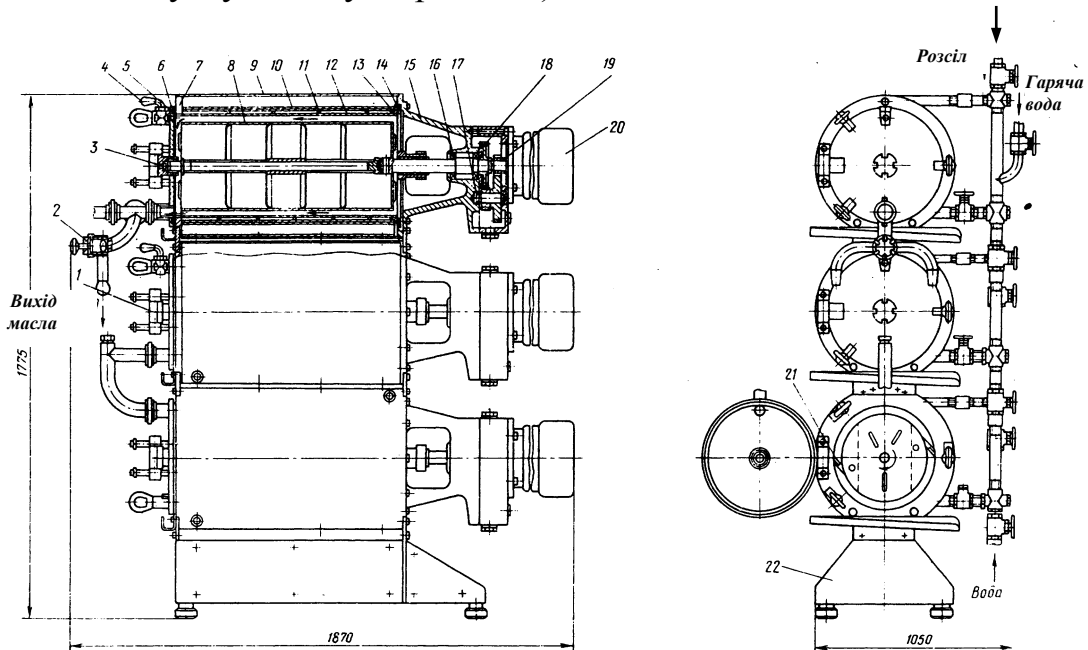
Загальний вид маслоутворювача марки Т1-ОМ-2Т:
